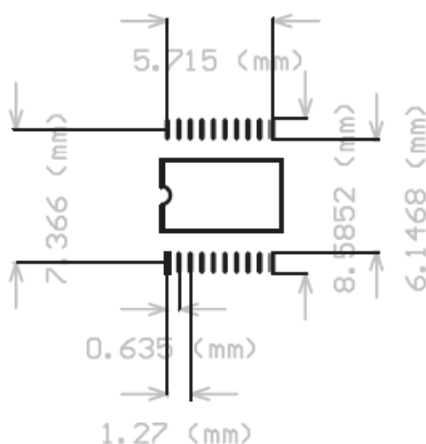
USB2I2C SSOP20 PCB 封装图（MM）
